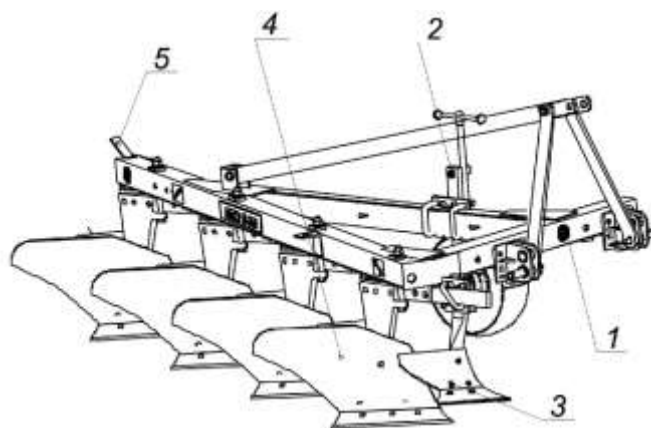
Плуг четырех корпусный навесной ПЛН-4-35: 1 – рама; 2 – механизм колеса; 3 – предплужник; 4 – корпус; 5 – световозвращатель
